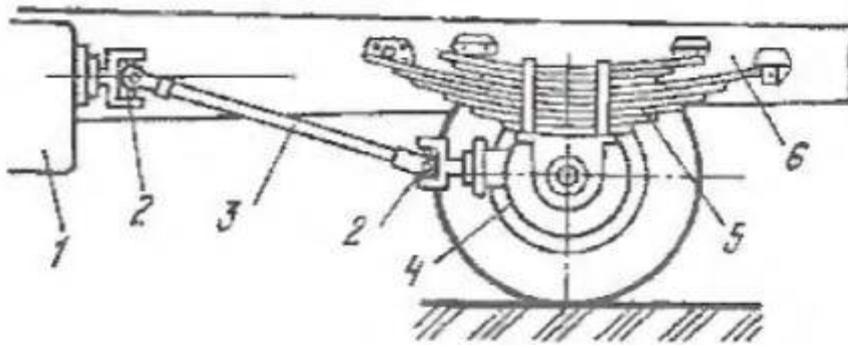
Схема карданной передачи: 1 — коробка передач; 2 — карданный шарнир; 3 — карданный вал; 4 — задний ведущий мост; 5 — рессора; 6 — рама
